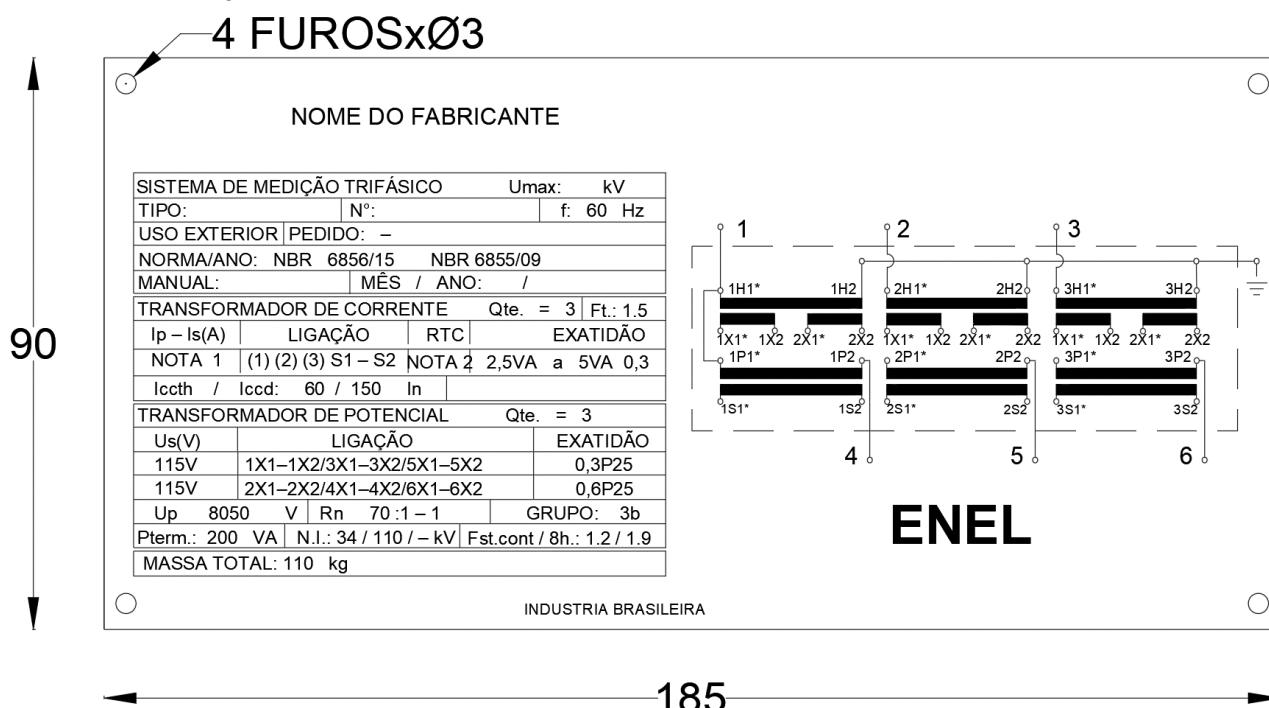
Placa de Identificação Instalada na Parte Frontal da Caixa Principal
